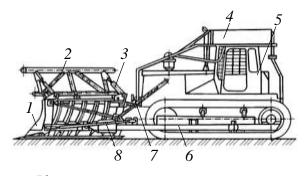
Кусторез МП-14: 1 – рабочий орган; 2 – толкательный брус; 3 – талреп; 4 – ограждение; 5 – базовый трактор; 6 – универсальная рама; 7 – заточное приспособление; 8 – раскос
